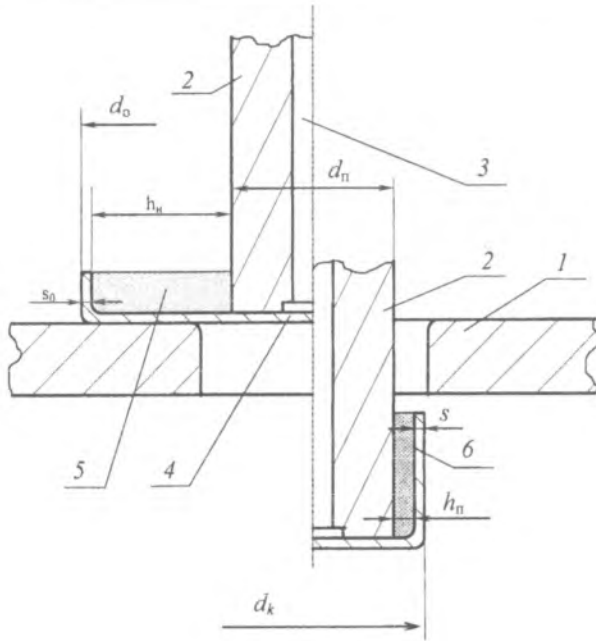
Схема процесса совместной вытяжки покрытия и основы: 1 – матрица; 2 – пуансон; 3 – съемник; 4 – металлическая заготовка; 5 – порошок; 6 – композиционное изделие
